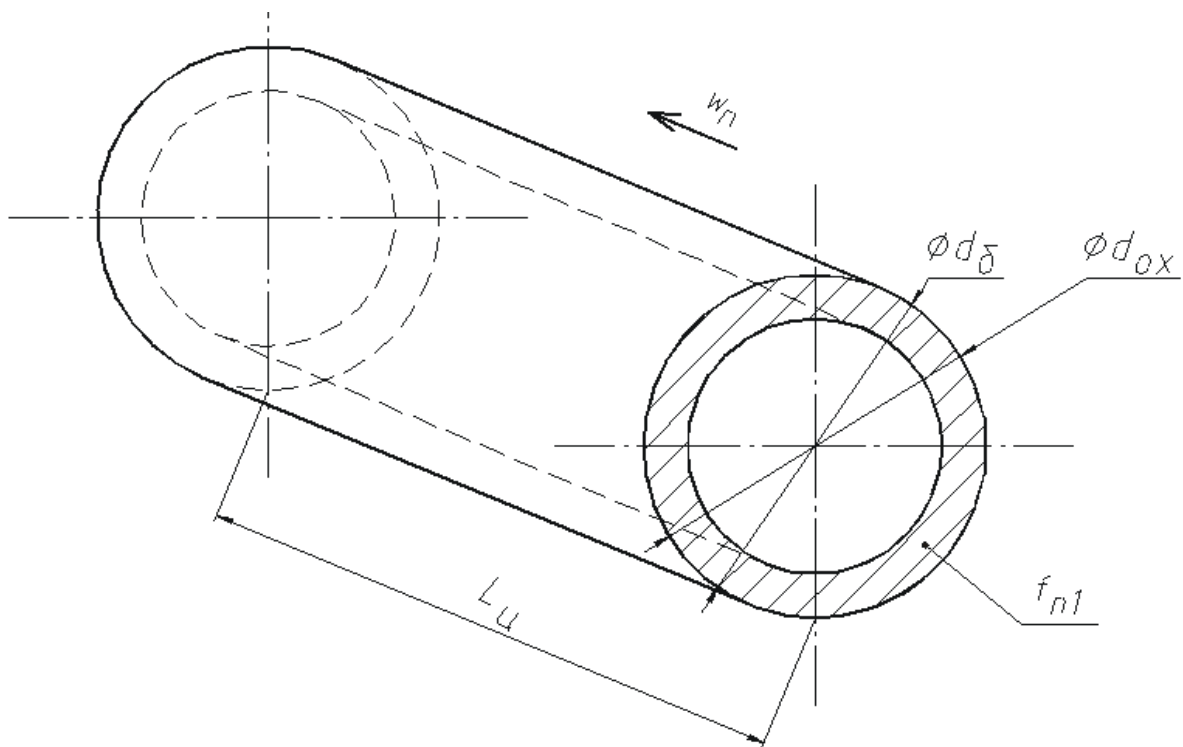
Розрахункова схема циліндра маслоутворювача.
